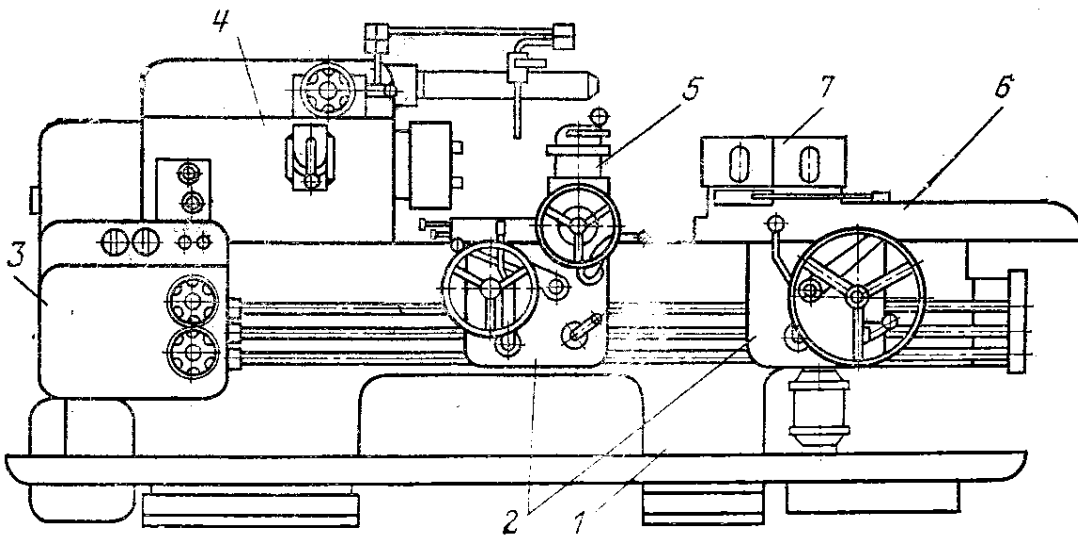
Загальний вигляд токарно-револьверного верстату 1П365.
